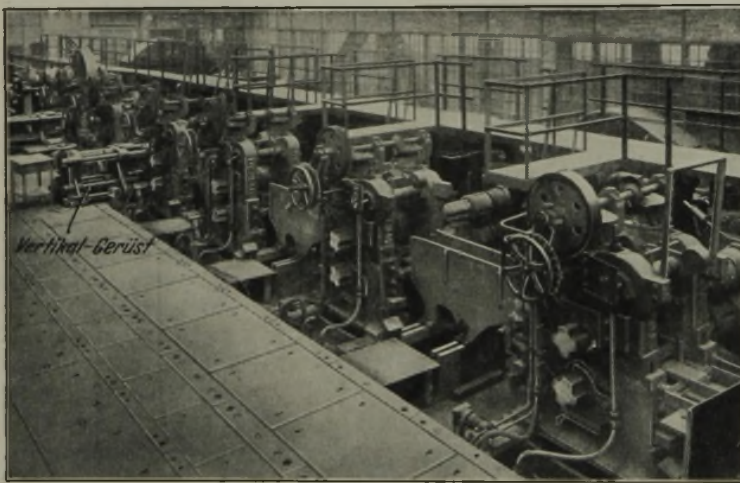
StraÙe 2 mit zwei Gruppen aus je sechs Gerüsten mit waagerechten Walzen und zwei Gerüsten mit senkrechten Walzen (Vertikalgerüsten) für Platinenwalzung.
